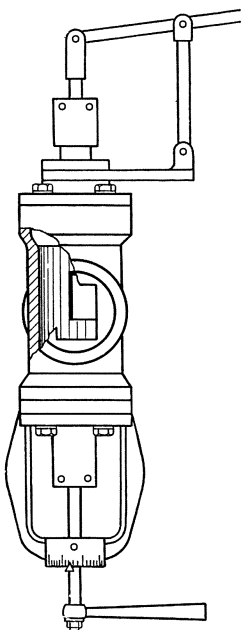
Regelventil von Carrick für Dampfantriebe.
